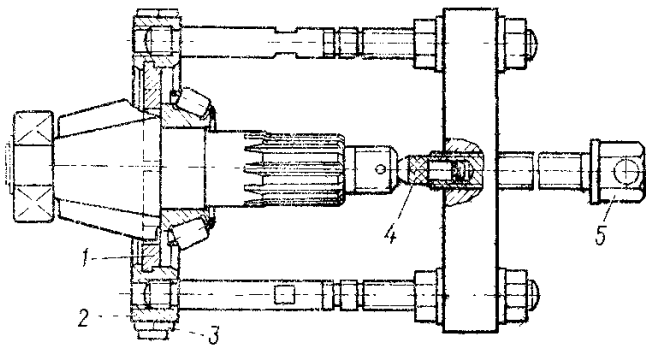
Снятие внутреннего кольца заднего конического подшипника ведущей шестерни: 1 — вкладыш; 2 — опора; 3 — гайка; 4 — центр; 5 — винт
